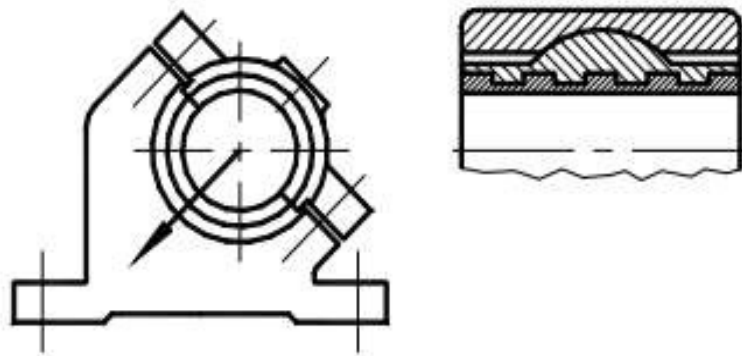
Роз'ємний самоустановлювальний підшипник
